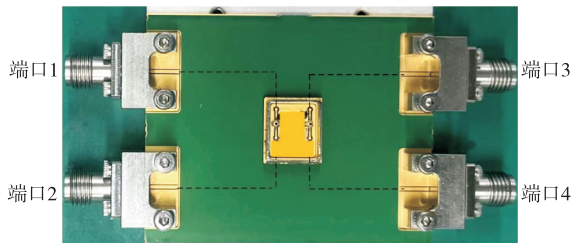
模组垂直互连结构与 PCB 测试板组装后的实物图
